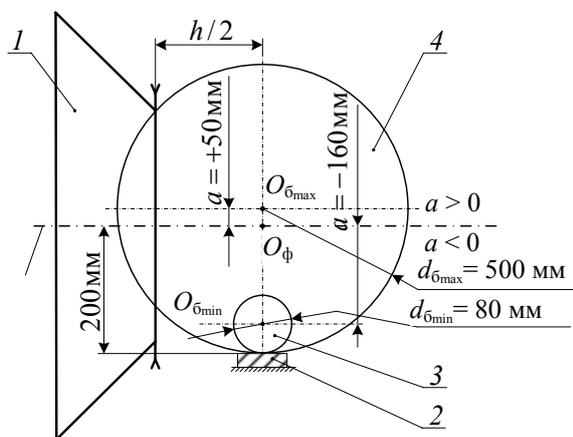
Схема обработки бревен на фрезерно-брусующем станке PSP 500 (SAB, Германия):
